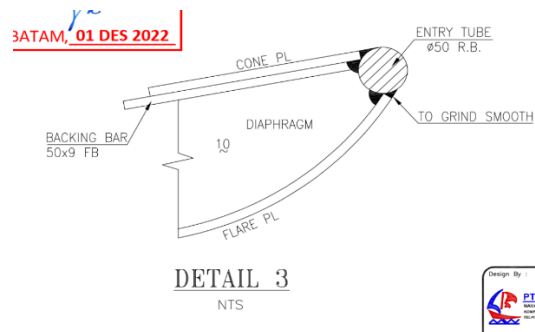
Dimensi Ukuran dan posisi *frame plate (backing bar plate)
